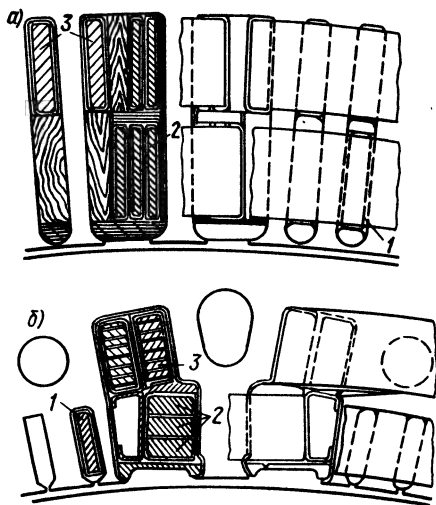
Обмотка статора двигателя однофазного тока: а — протяжного исполнения; б — в виде катушек
